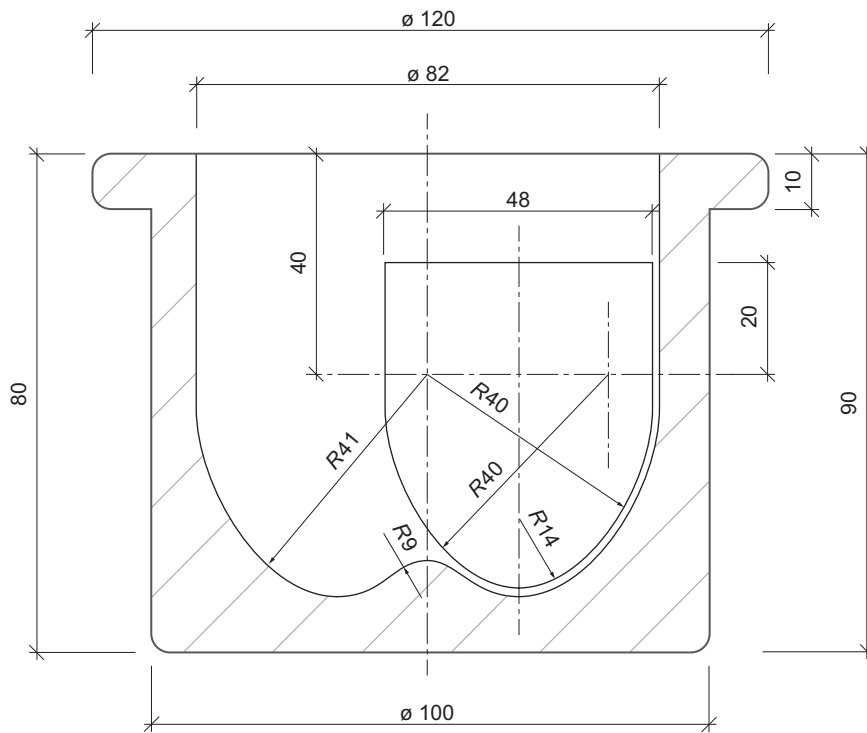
Moule pour éprouvettes 10 mm x 10 mm x 40 mm (dimensions en millimètres)
